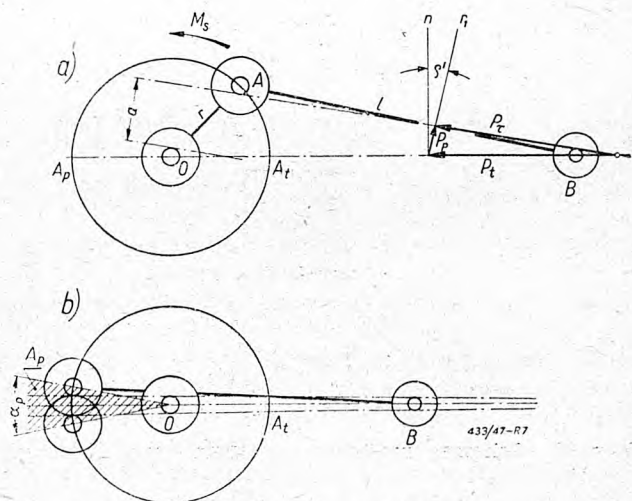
Schemat mechanizmu włączającego podwójnego sprzęgła stożkowego.
